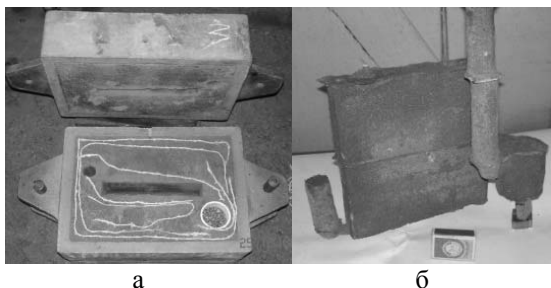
Литейная форма для изготовления двухслойной отливки типа вертикальная плита перед заливкой расплавом (а) и общий вид отливки (б)
